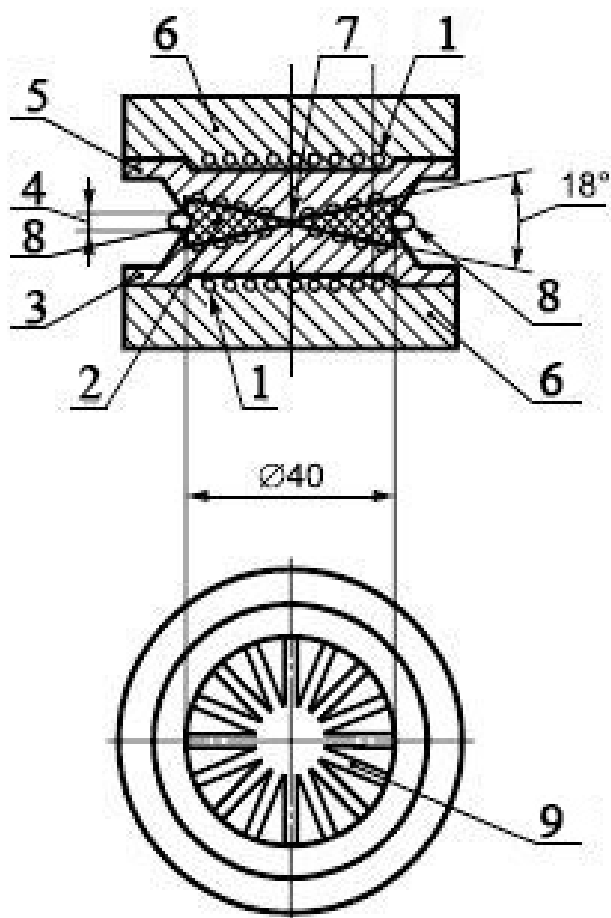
Испытательная камера безроторного вулканетра: 1 – нагреватель, 2 – образец для испытания, 3 – нижняя полуформа, 4 – зазор, 5 – верхняя полуформа, 6 – температурный датчик, 7 – зазор, равный 0,5 мм, 8 – излишки образца, 9 – канавки
